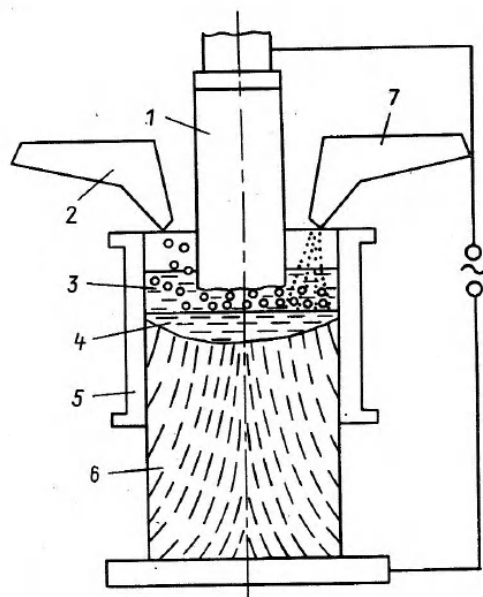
Схема электрошлаковой плавки металлизированных окатышей: 1 - нерасходуемый электрод; 2 - дозатор подачи окатышей; 3 - расплавленный шлак; 4 - металлическая ванна; 5 - кристаллизатор; 6 - наплавленный слиток; 7 - дозатор подачи лигатуры и раскислителей
